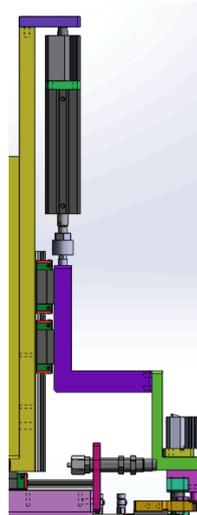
Máquina de separación de junta tórica 3. Fuente:propia
